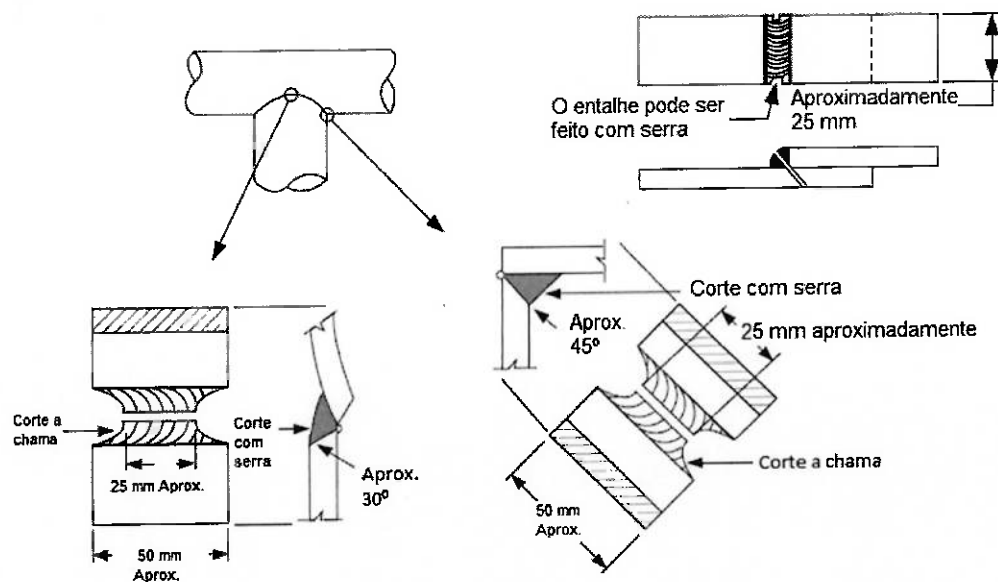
Corpos de Prova para ensaios de Nick-break para juntas de ângulo para qualificação de procedimento e de soldador conforme API 1104 [3].
